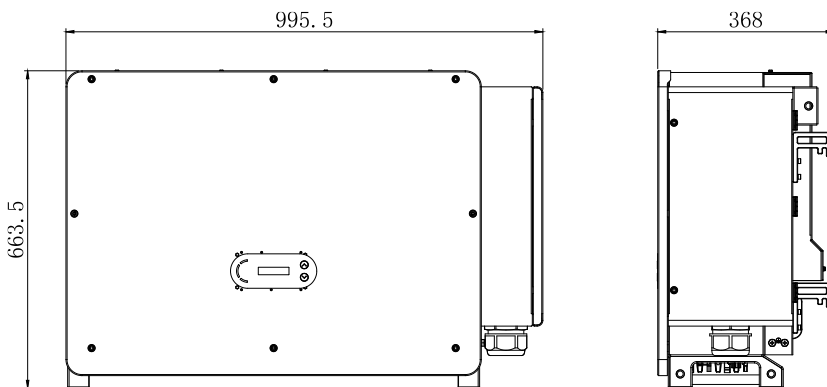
Dimensiones de la vista frontal y de la vista izquierda del producto
